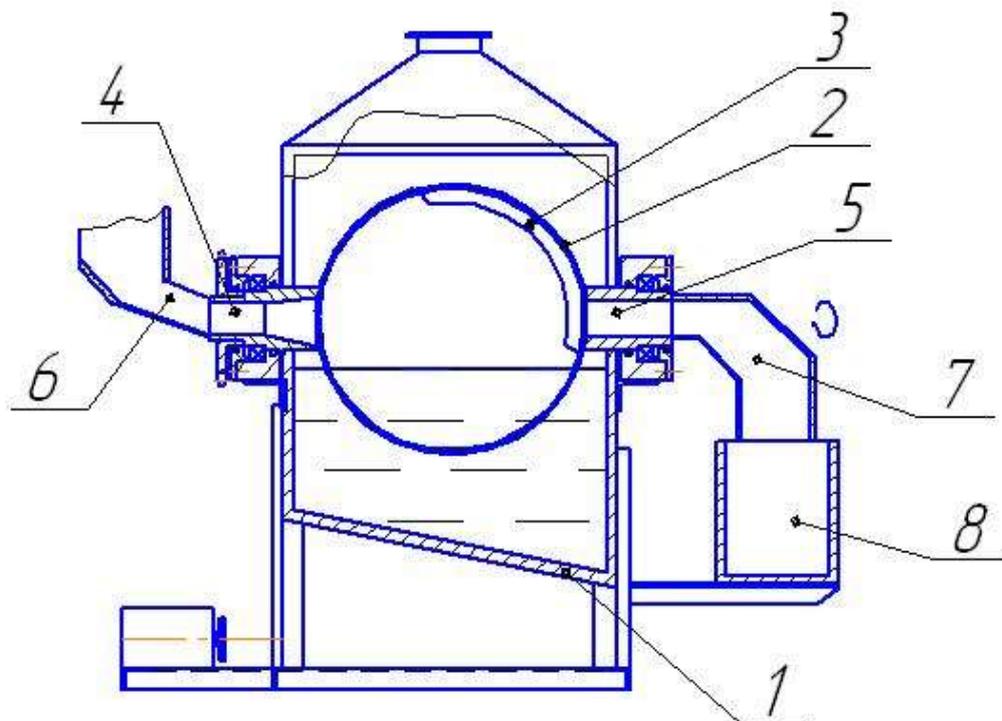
Установка для очистки изделий (АС 521031)
